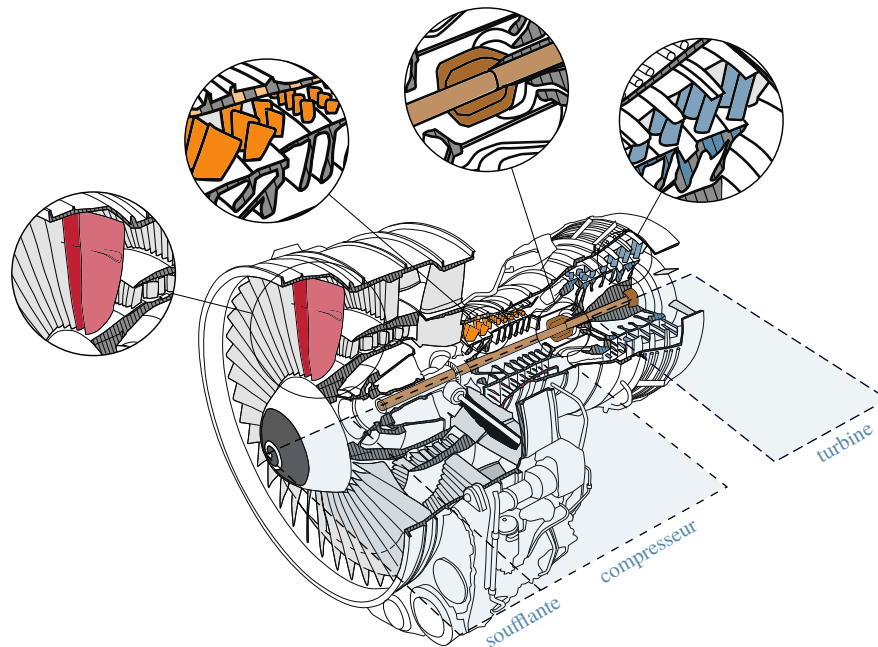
Interfaces de contact au sein d'une turbomachine et étages (■) de la turbomachine. Adaptée de [59].
